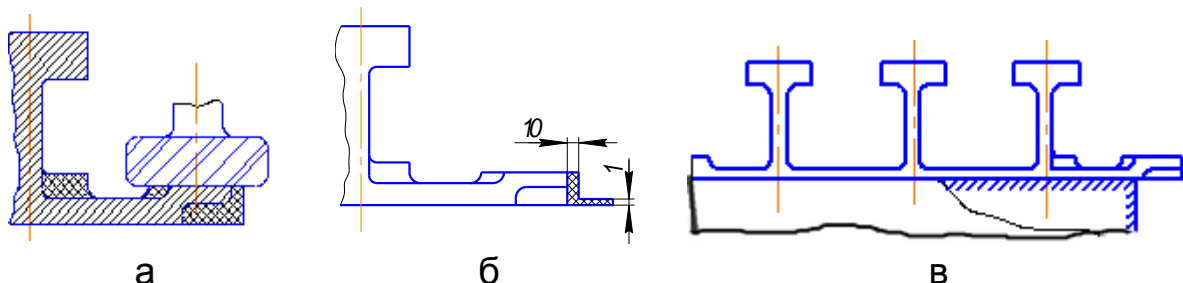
Схеми оброблення замкової частини на закінцівці заготовки панелі
